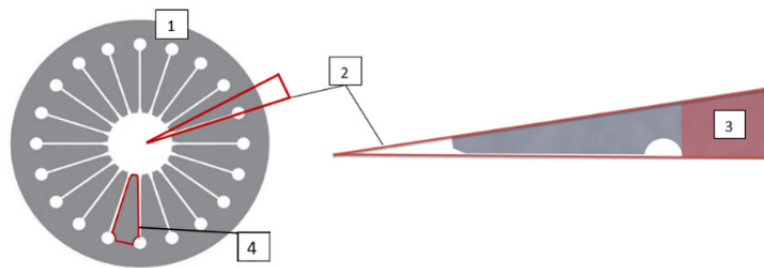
Схематическое представление постановки задачи: 1 – общий вид изделия; 2 – область моделирования; 3 – зона нагрева; 4 – палец демпферной пружины
